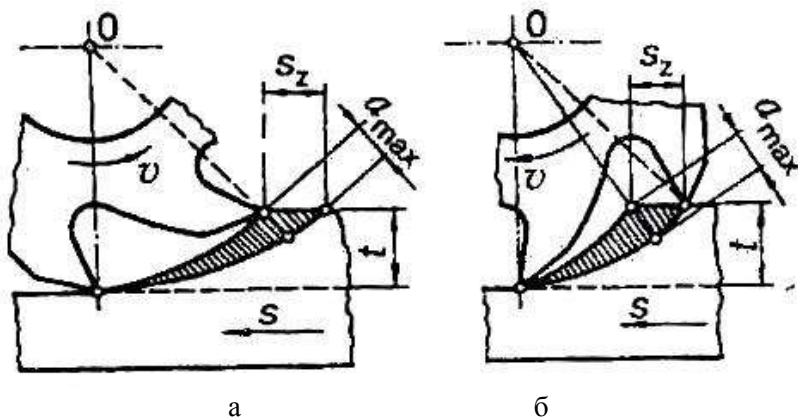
Зустрічне (а) та попутне (б) фрезерування
